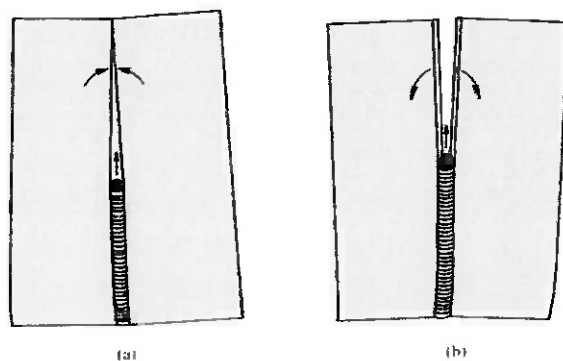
Rotação durante a soldagem para (a) baixo e (b) alto aporte térmico.
